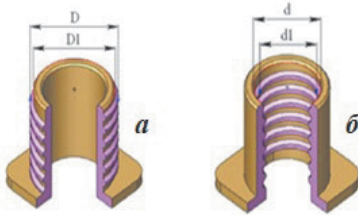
Різьба: а — зовнішня; б — внутрішня
